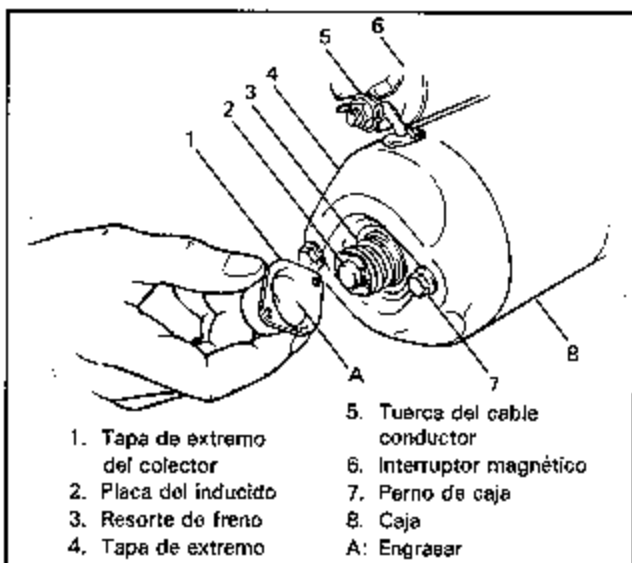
G-14 Instalación de la Tapa de Extremo del Colector
